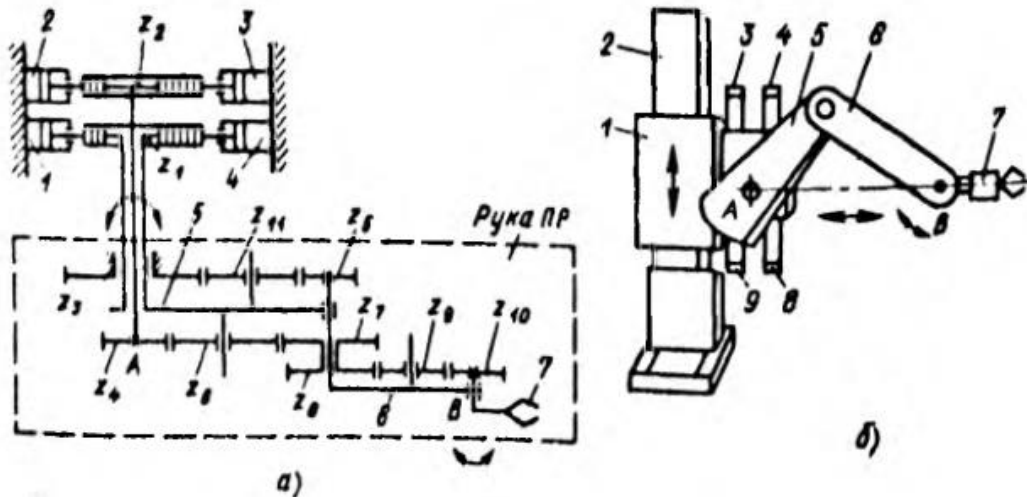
Важільно – зубчастий механізм руки ПР
